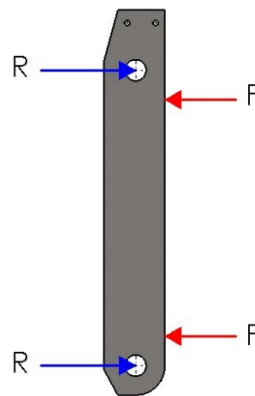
Distribución de cargas en la viga vertical con taladros (Fuente: propia)
